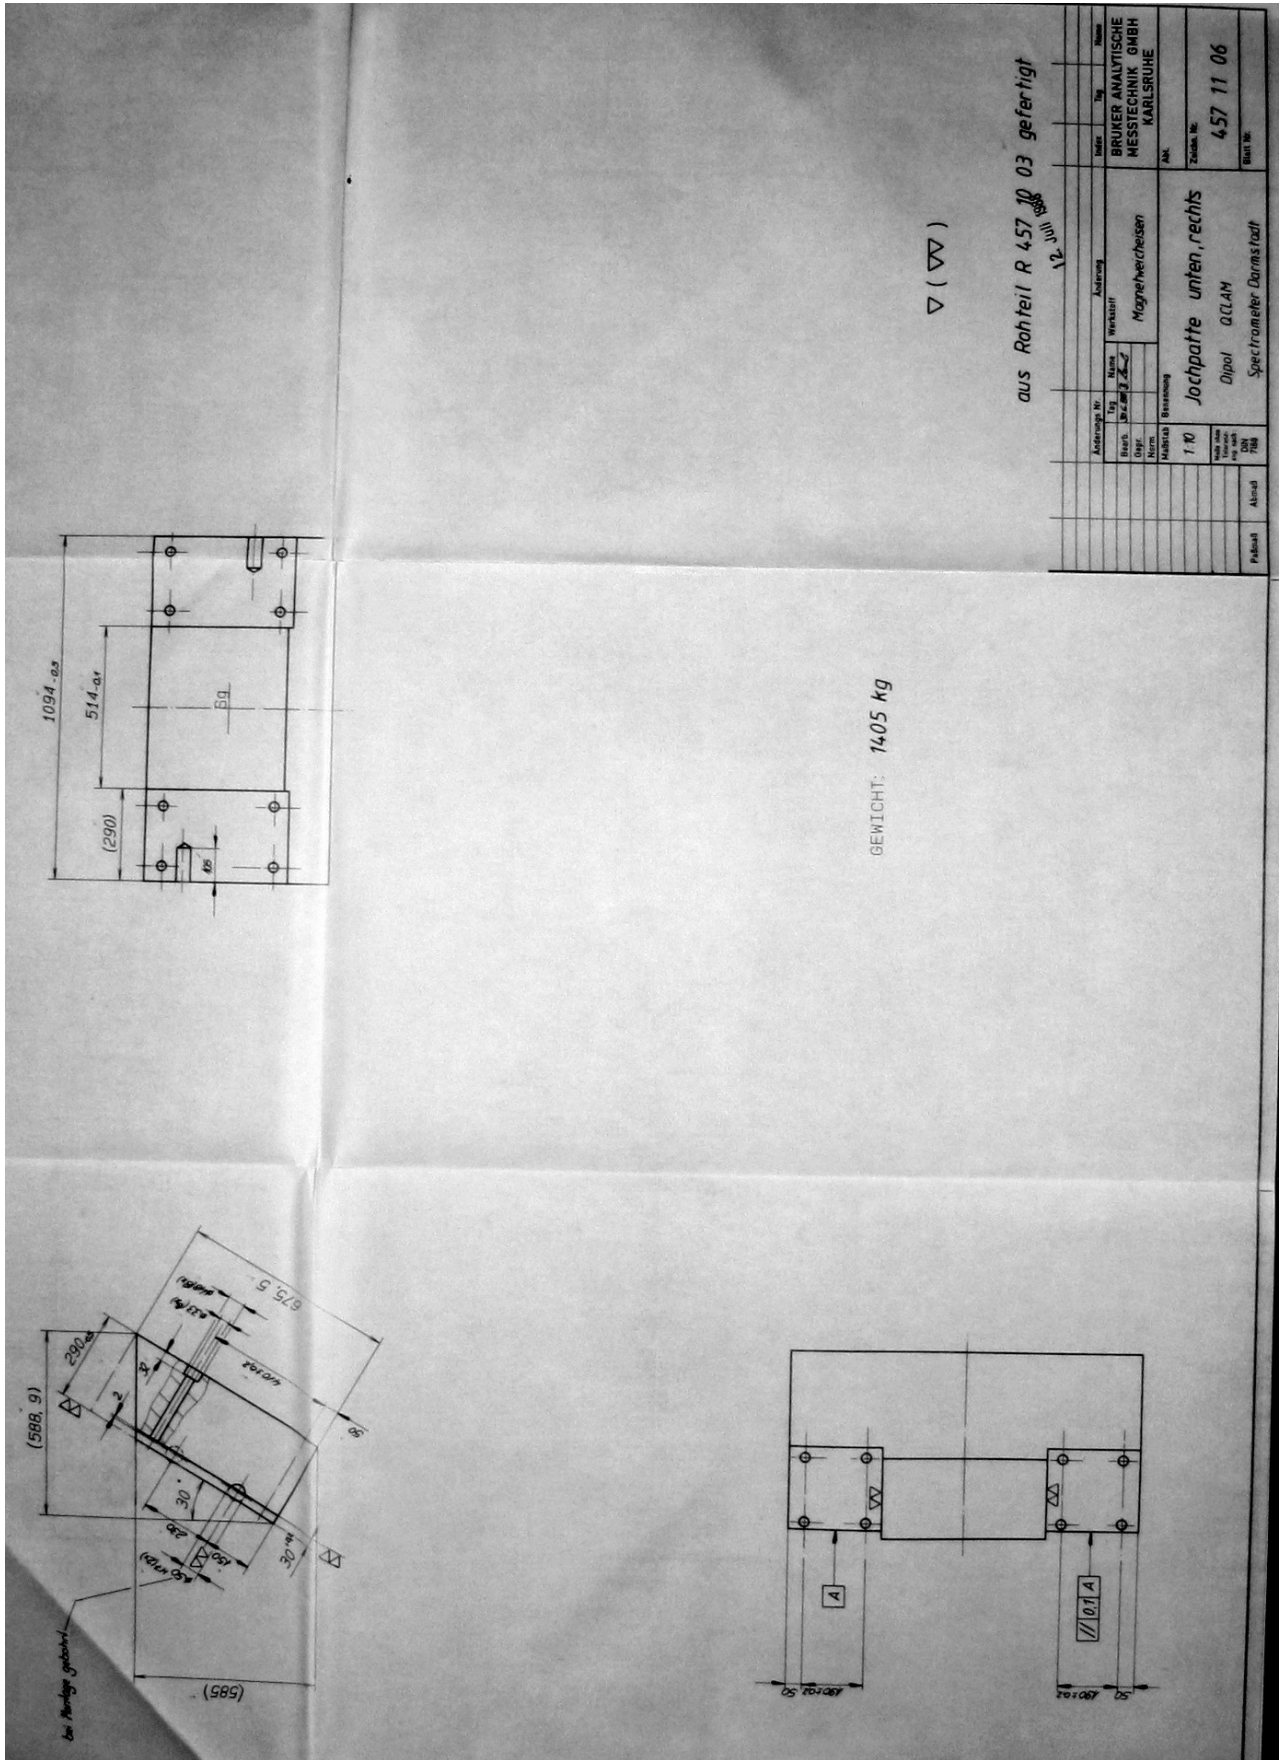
Technische Zeichnung der rechten unteren Jochplatte des QClams.
